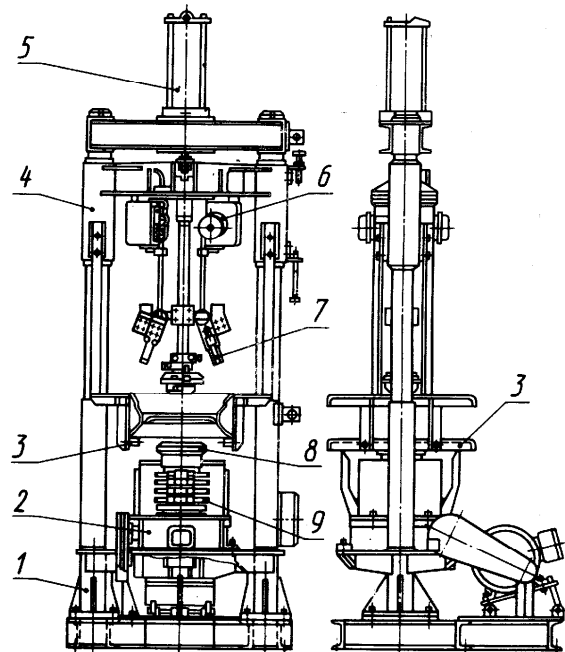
Станок-автомат для сварки тракторных колес
